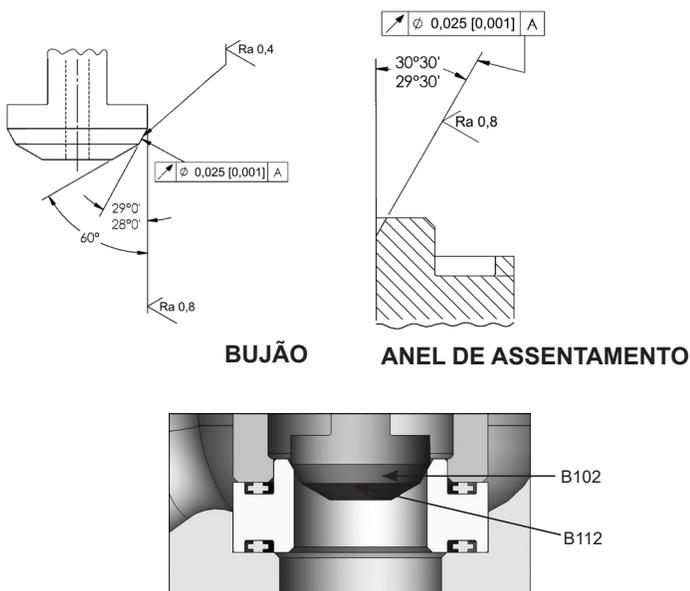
Superfícies de assentamento do bujão e do anel de assentamento
